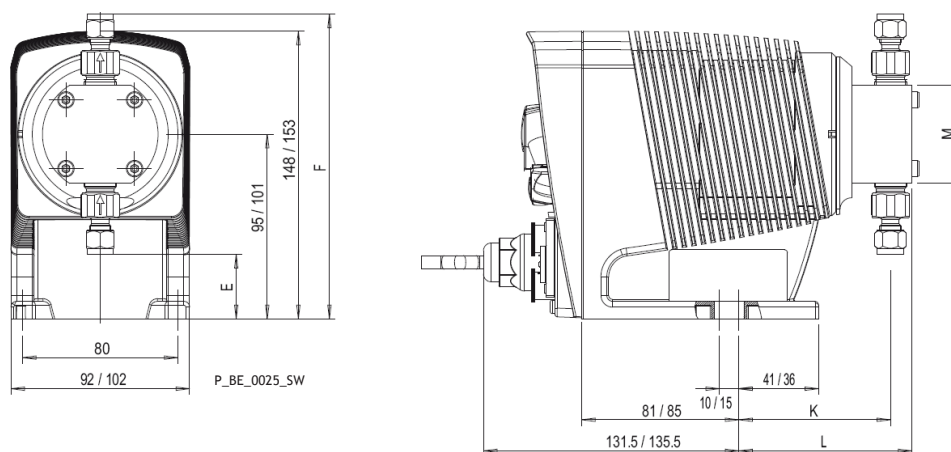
Размерный чертеж Beta® BT4b/BT5b, Материал конструкции SS – размеры в мм
